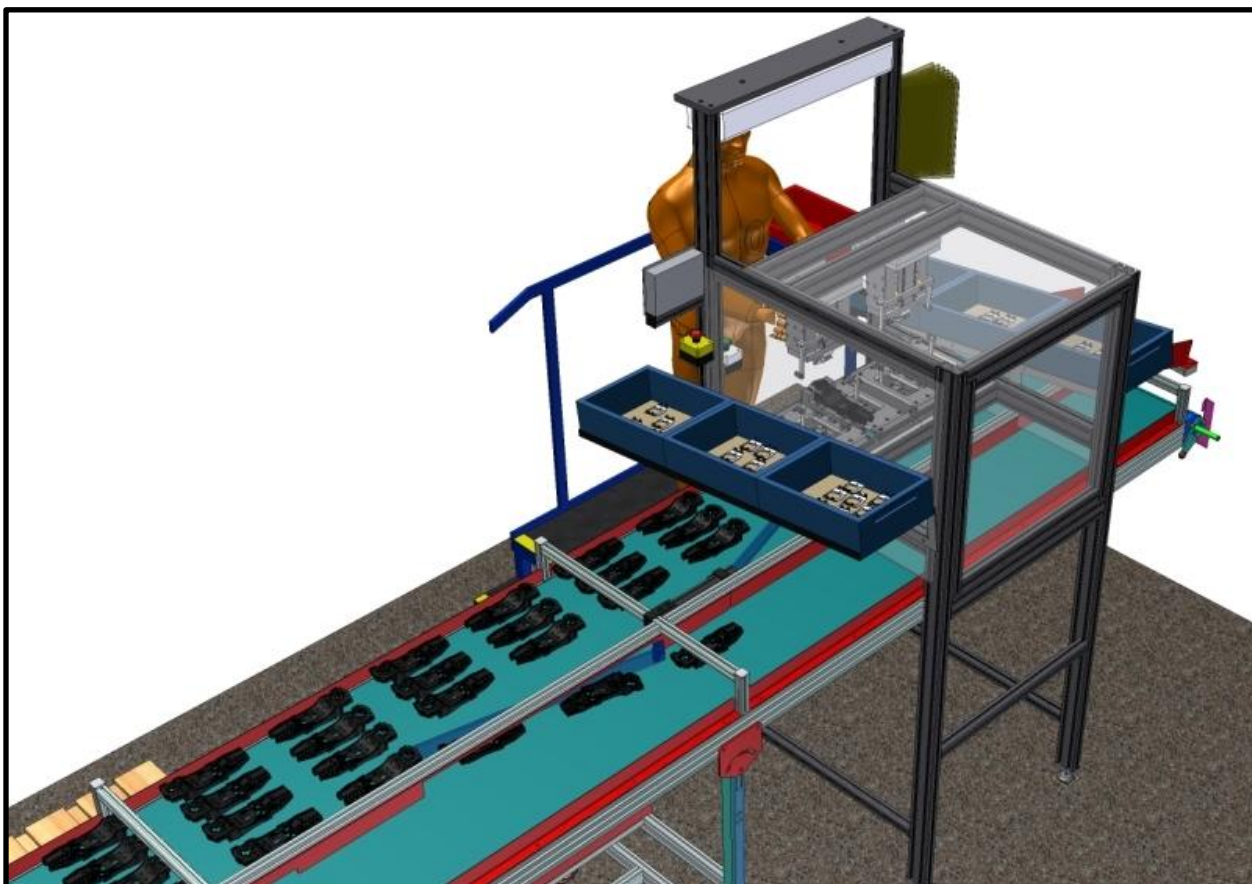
Konstrukce lisovacího stroje – Pohled 1
